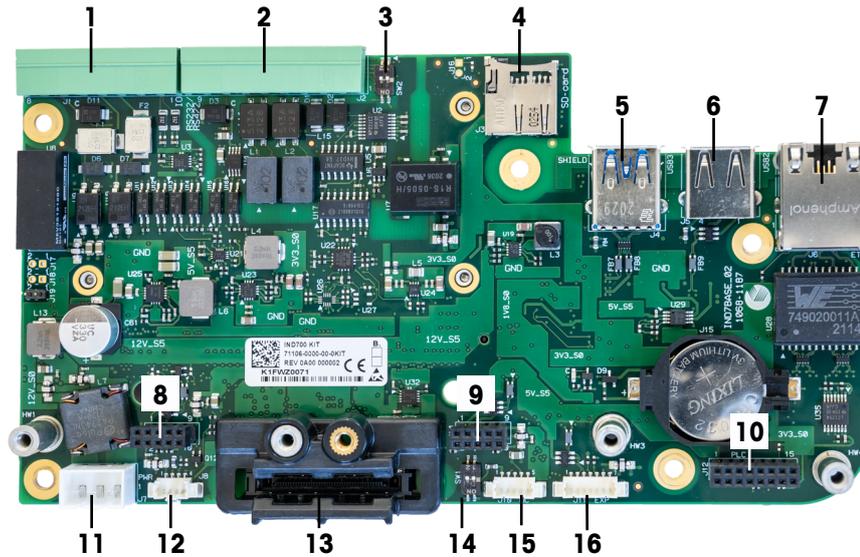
Conexões e Interruptores da PCB Principal do IND700
